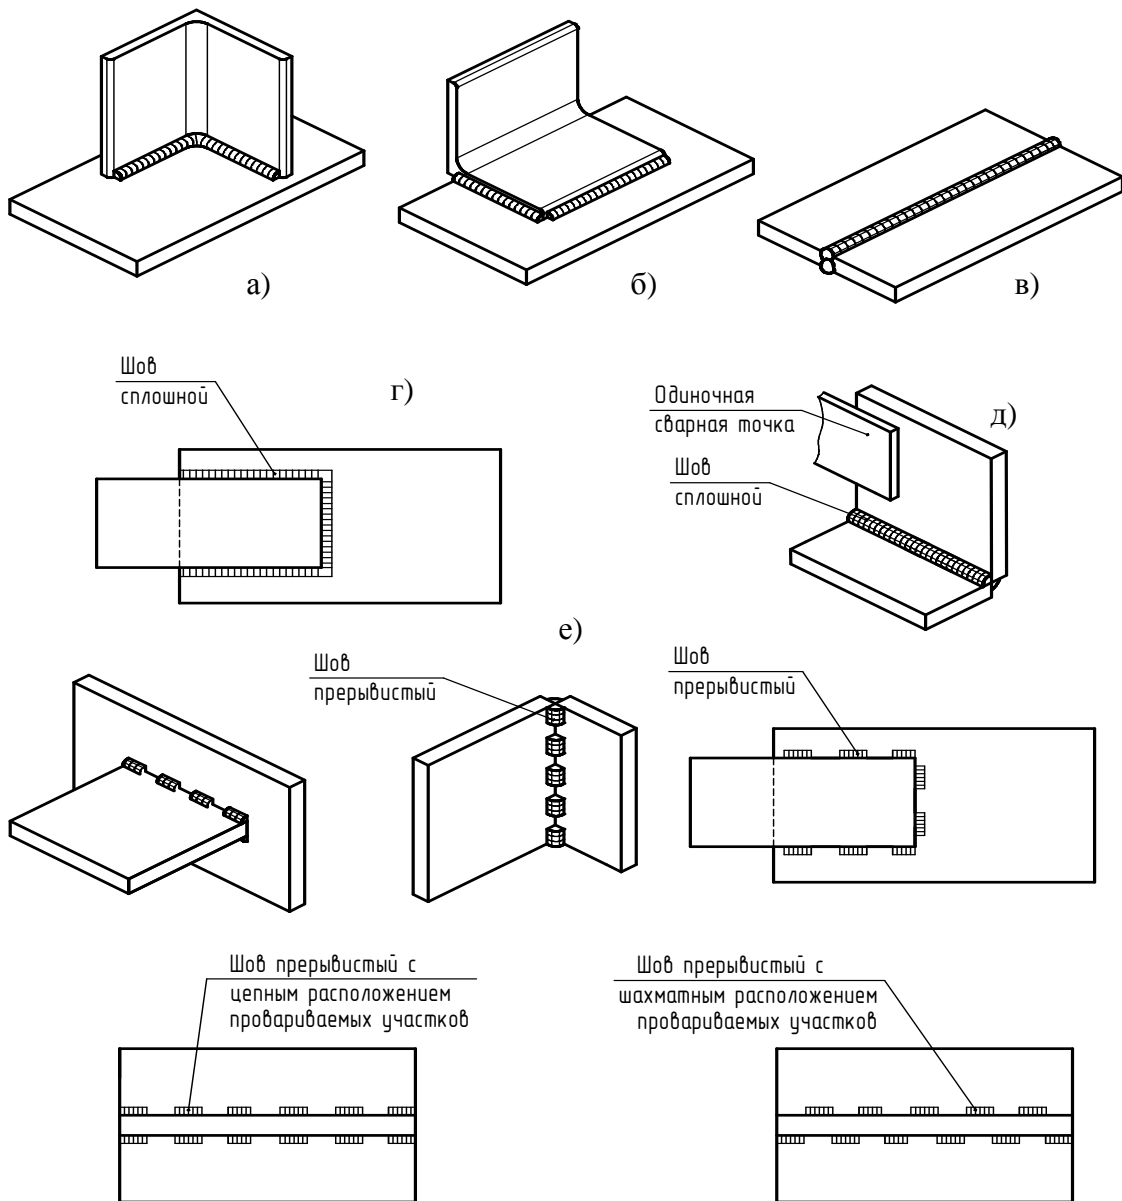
(а, б, в, г, д, е). Виды сварных соединений
